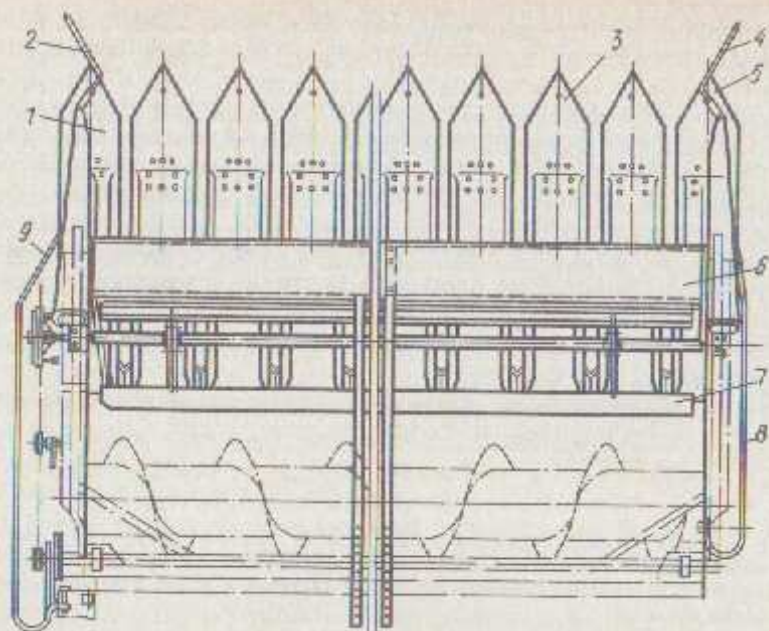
Приспособление для уборки подсолнечника на зерно:
